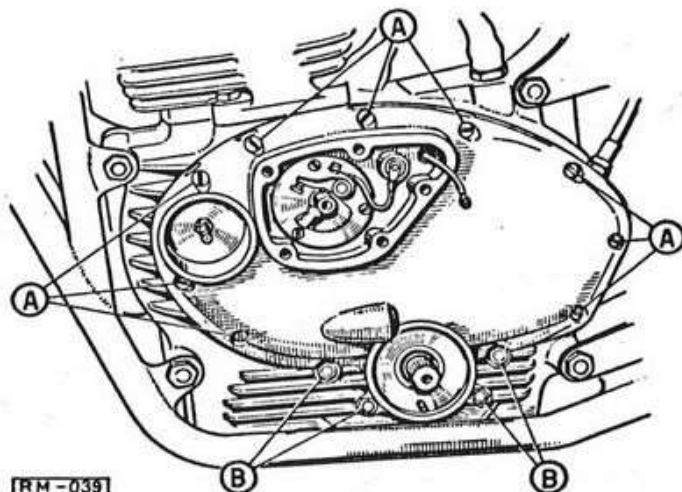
Smontaggio coperchio lato sinistro motore.
